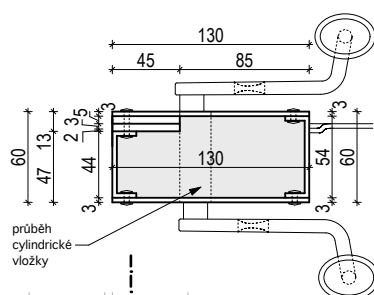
KOVANÝ ZÁMEK BRÁNY
